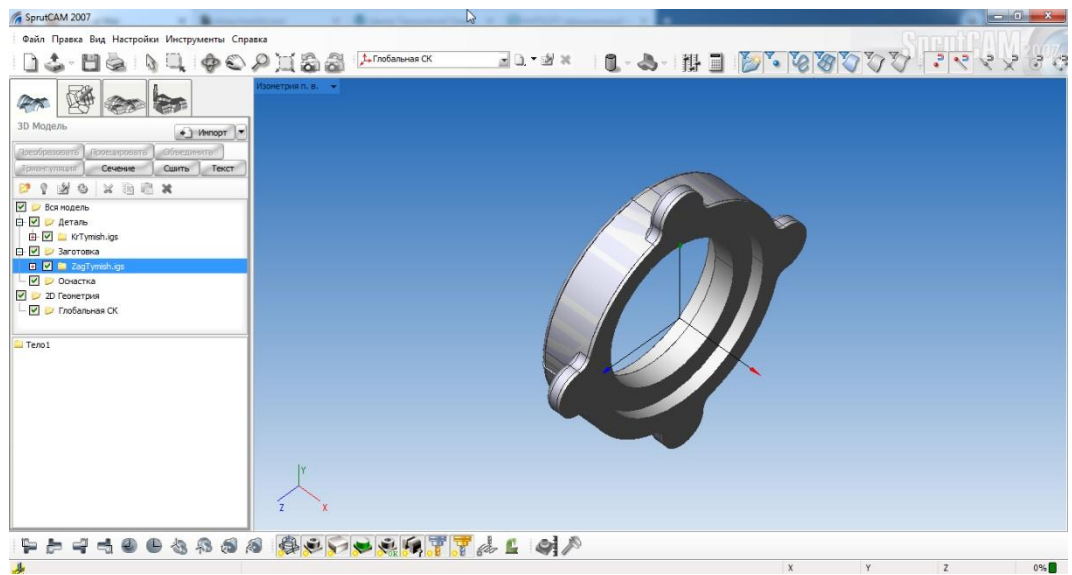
Деталь та заготовка, імпортовані для проведення проектування
